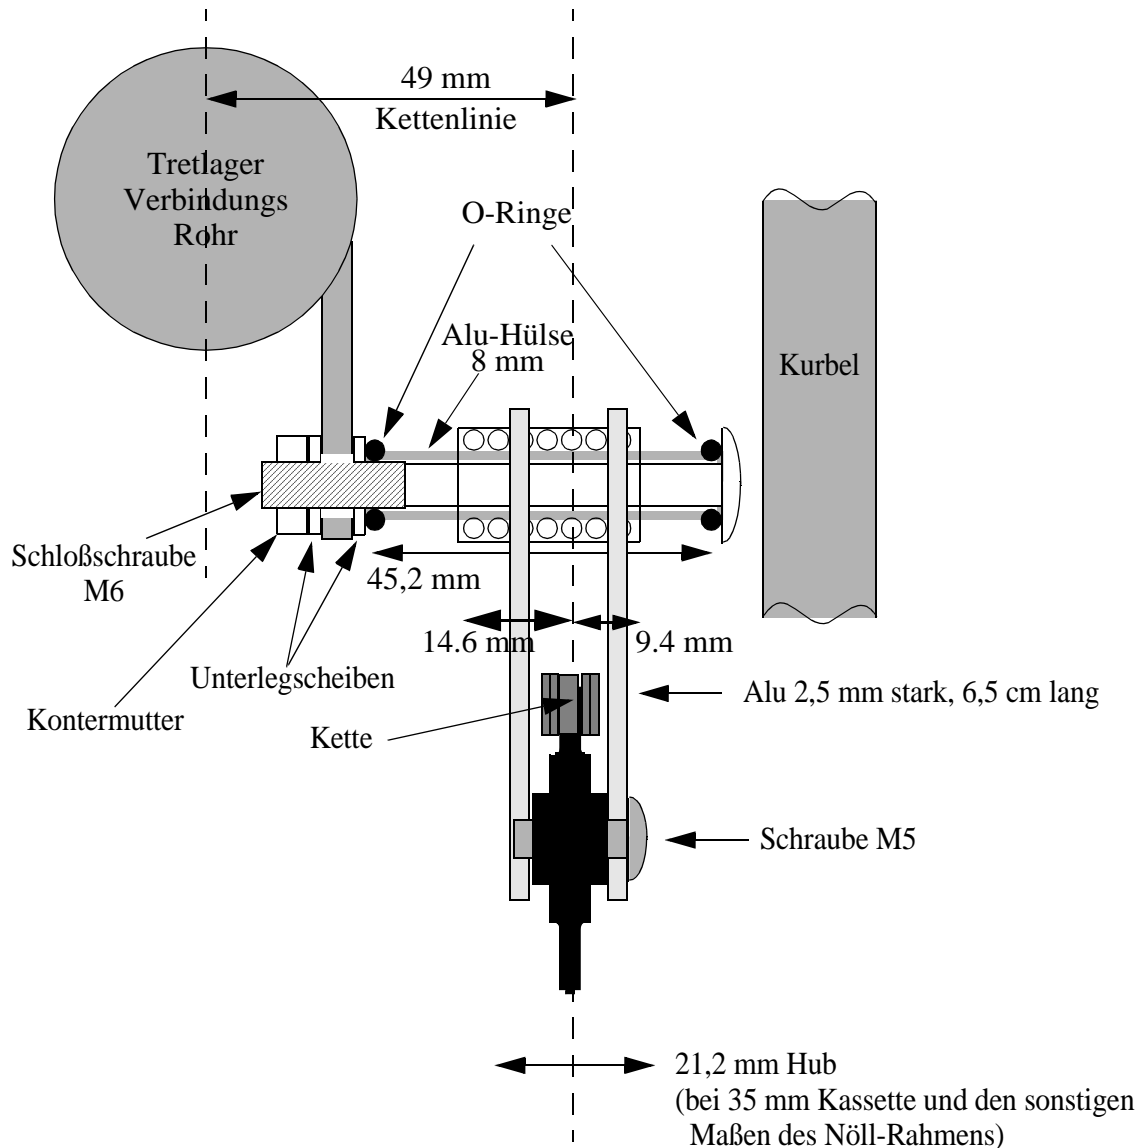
zeigt die Draufsicht der Kettenrolle in Fahrtrichtung.
